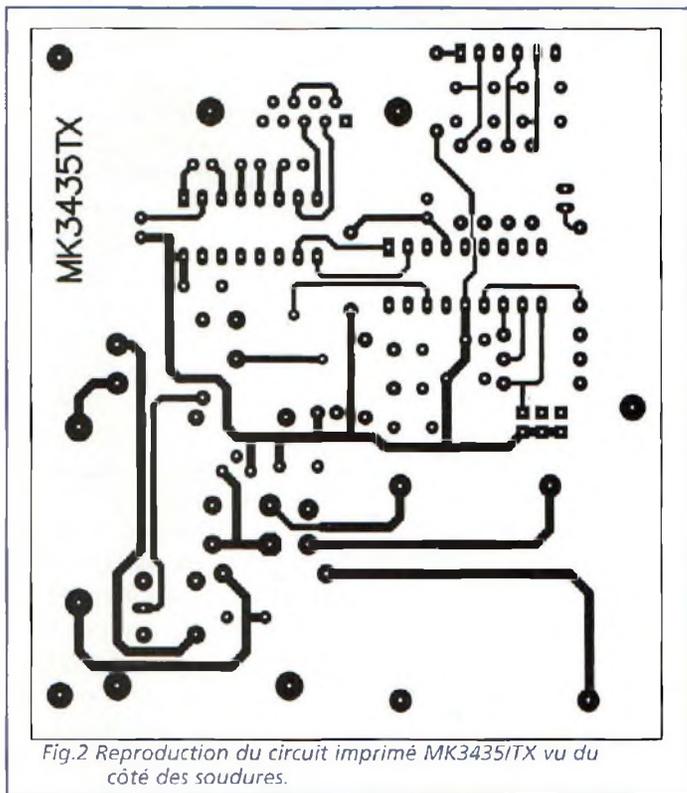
Reproduction du circuit imprimé MK3435/TX vu du côté des soudures.
